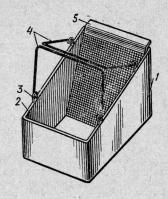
I — корпус; 2 — отбортовка; 3 — проушина; 4 — ручки; 5 — сетка
